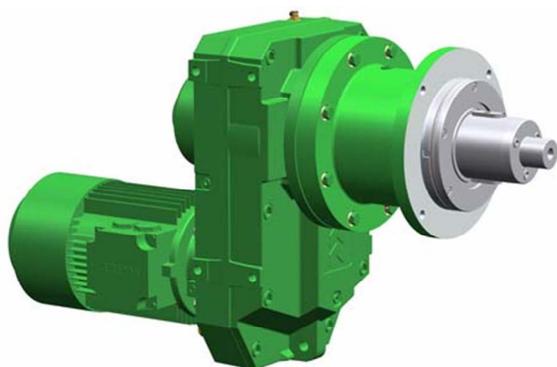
Мотор-редуктор WATT AVS 85A 114ML4 TH с дополнительным подшипниковым узлом
